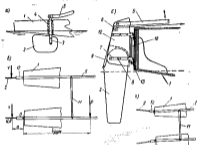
Конструкция рулевого устройства: а — подвесной боковой руль; б — съемный руль с выдвижным удлинителем; в — простой откидной рулевал; г — рулевое устройство с разным углом перекачки рулей; д — шкатор; е — степс; ж — баллер; з — гальванический корпус; и — ручка; к — шток; л — оськи рулевой шкаторы; м — ось мачты; н — шкатор; о — шток; п — подвески; q — дощечки шкаторы; р — рулевая тяга.
